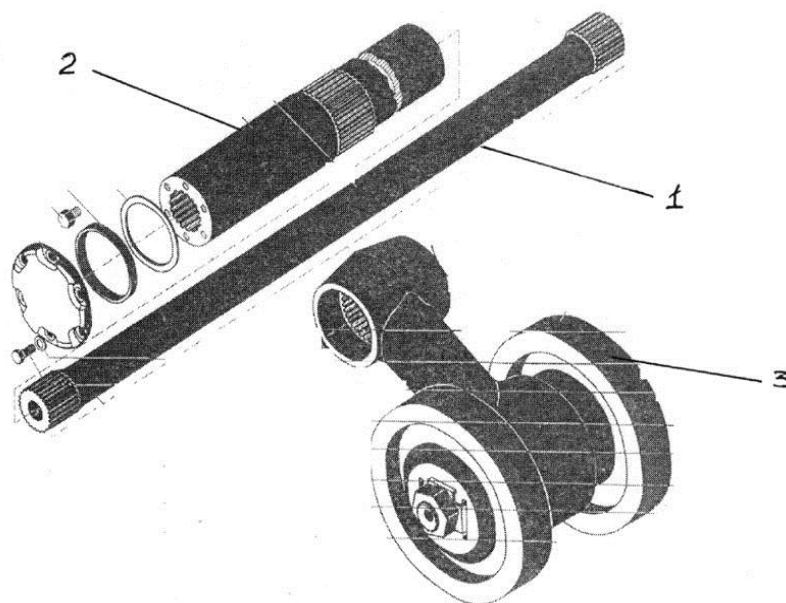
Подвеска трактора ДЭТ-250М: 1 - торсионный вал; 2 - труба балансира; 3 - каток с балансиром
